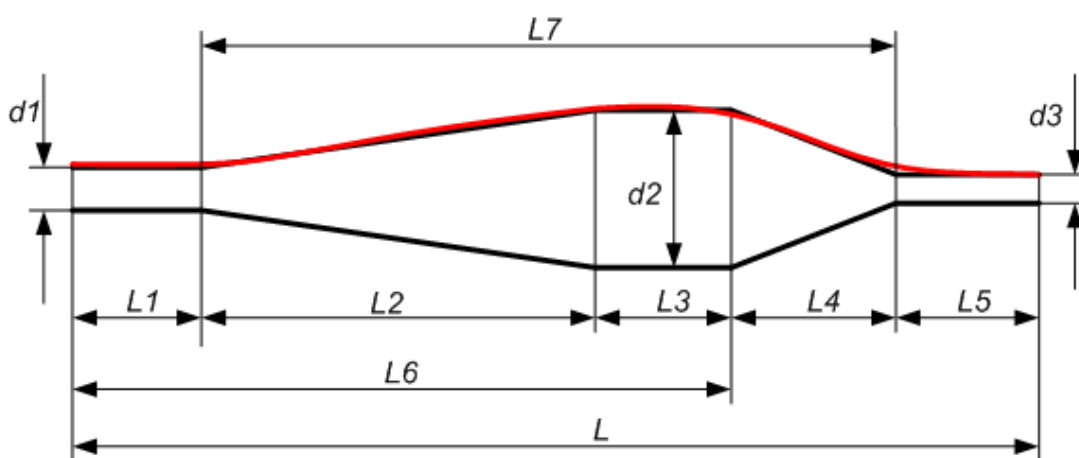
Ориентировочные размеры рассчитываемого резонатора
